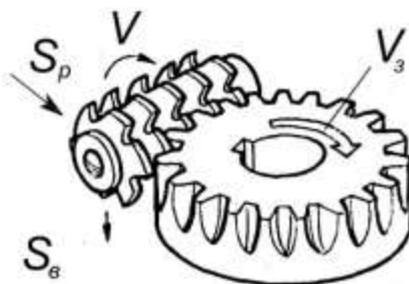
Схема нарезания зубчатых колес червячной фрезой.
